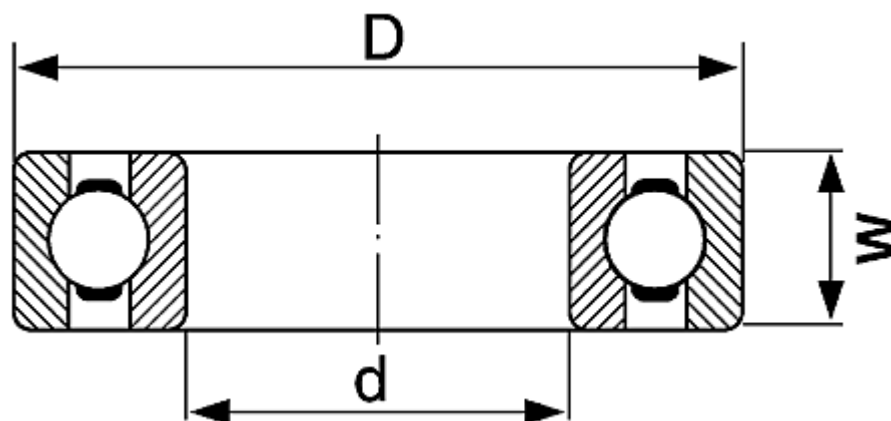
Rulment cu bile E2.XXXX-2Z
